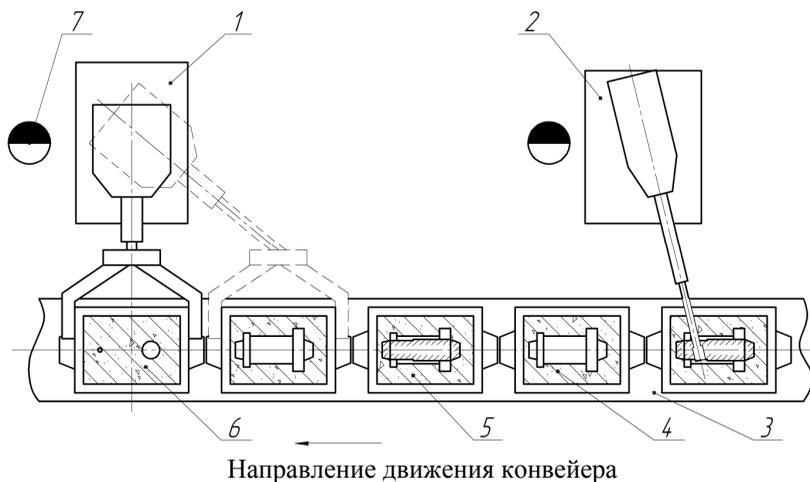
Роботизированный комплекс сборки литейных форм: 1 – робот-сборщик литейных форм; 2 – робот-проставщик стержней; 3 – литейный конвейер; 4 – верхняя полуформа; 5 – нижняя полуформа; 6 – литейная форма в сборе; 7 – операторы РТК
